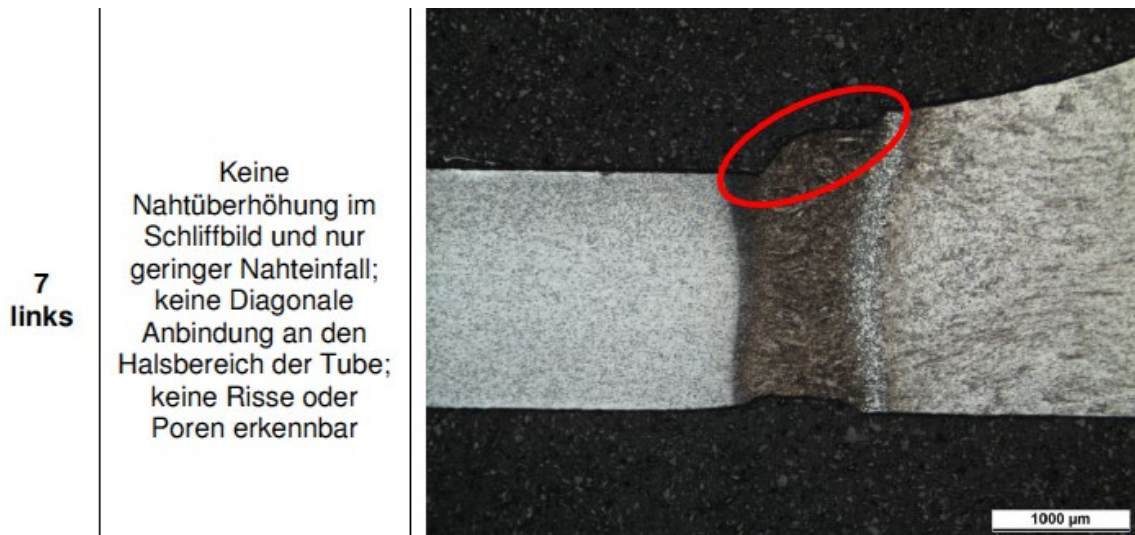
Querschliff der Probenr. 7 mit galvanisch beschichteter Flanke der Tube
